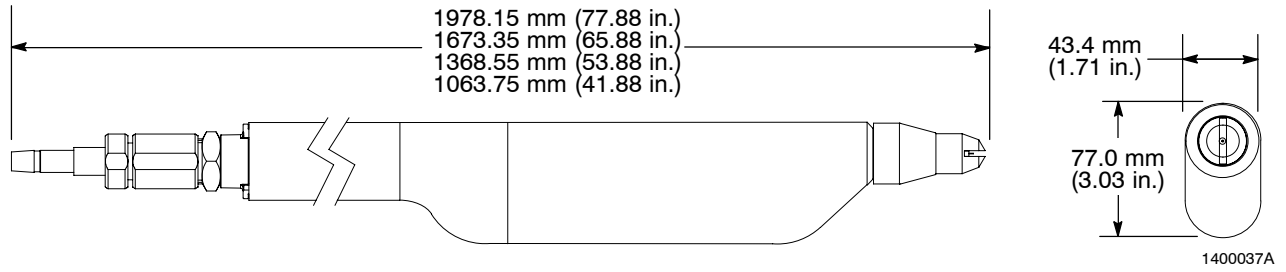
Dimensioni della pistola con montaggio su tubo
